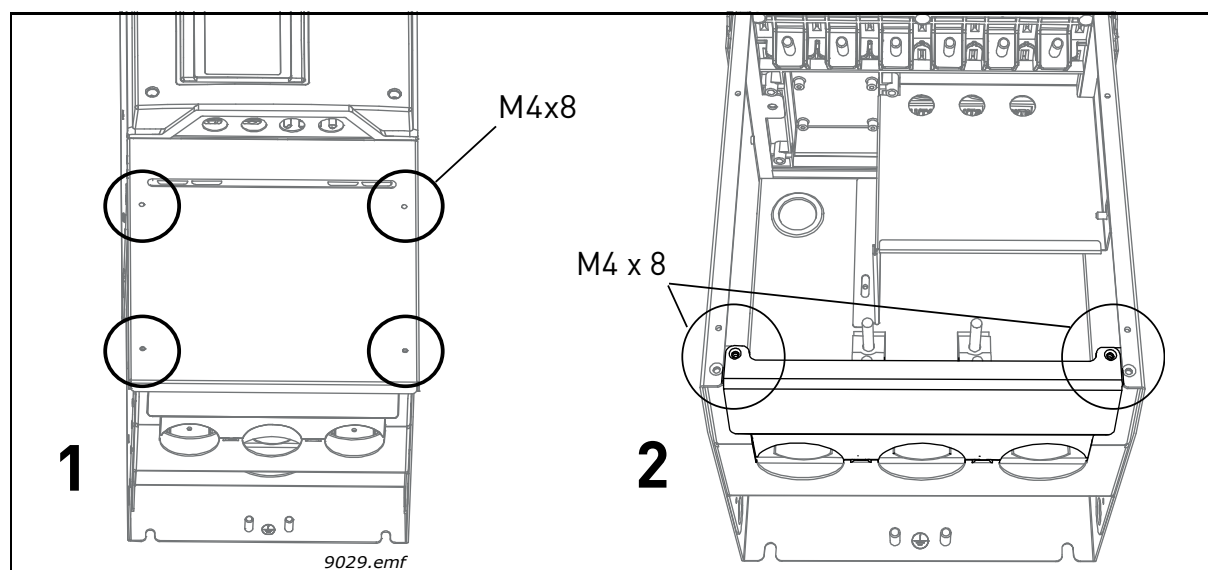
Снятие крышки кабельного отсека и кабельной планки (MR8).
